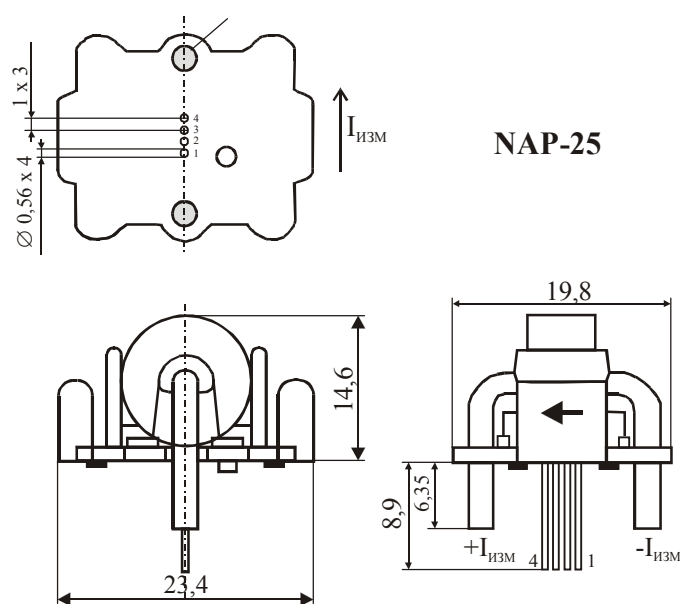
Внешний вид и габаритные размеры датчиков тока типа NAP-25
